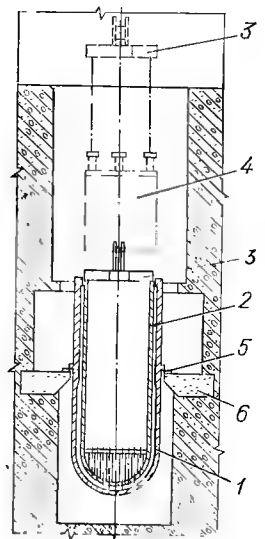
Установка шахты и выгородки в корпус реактора.
